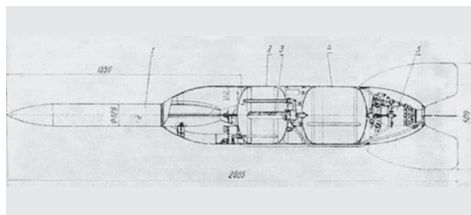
Схема ракеты Р-05 с высотой подъема 50 км: 1 – устройство для открывания парашюта; 2 – парашют; 3 – приборы; 4 – бак горючего; 5 – ПАД; 6 – бак окислителя; 7 – двигатель; 8 – стартовые пороховые двигатели (сбрасываемые). Разработка КБ № 7 по заданию Геофизического института АН СССР, 1937– 1938 гг.
